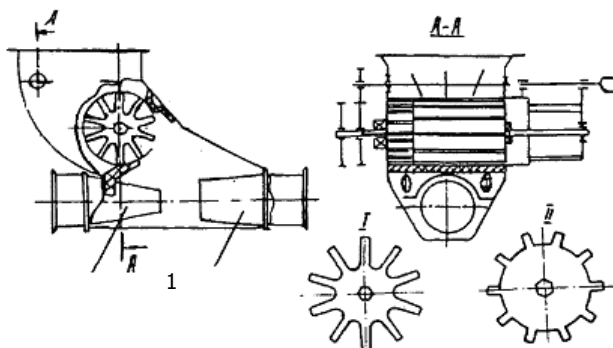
Схема высевающего аппарата зерновой пневматической сеялки с избыточным давлением
